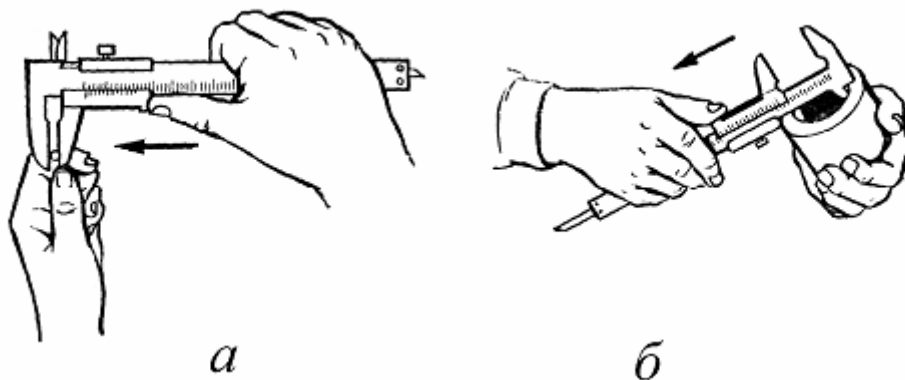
Измерение штангенциркулем наружных (а) и внутренних (б) размеров незакрепленной детали
